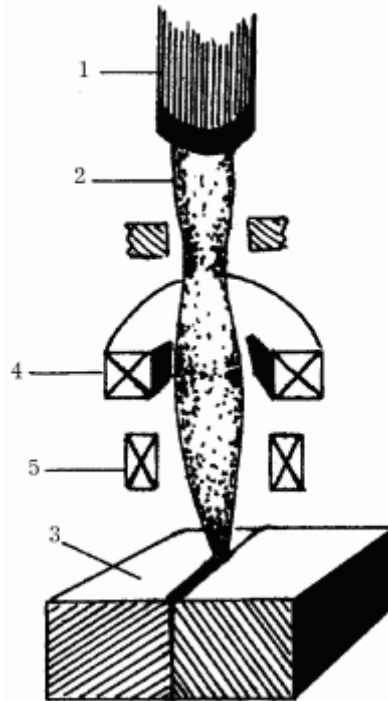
Электронно-лучевая сварка: 1 – катод; 2 – пучок; 3 – соединяемые заготовки; 4 – магнитная линза; 5 – катушка.
